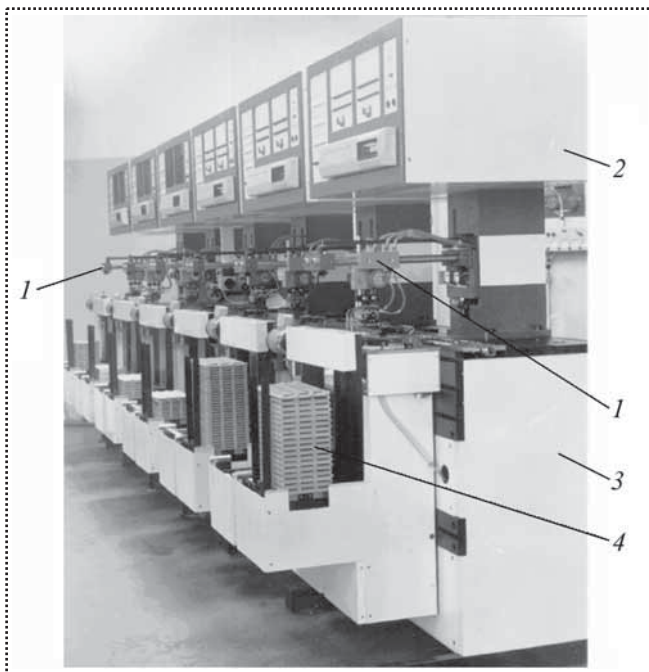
Внешний вид линии модульного типа с кассетными накопителями деталей для сборки металлокерамических корпусов ИМС:
